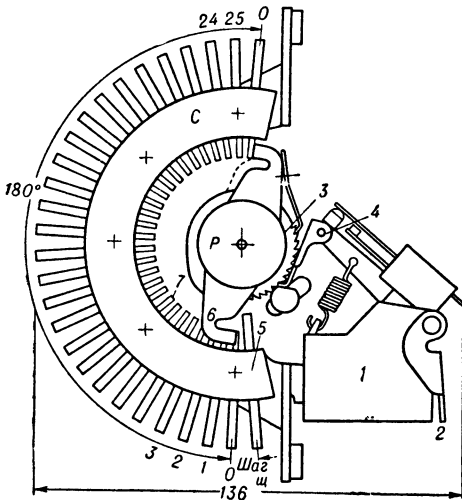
Искатель типа ШИ (эскиз): 1 — катушка электромагнита; 2 — якорь; 3 — храповое колесо; 4 — собачка храпового колеса; 5 — контактная группа; 6 — щетка; 7 — контактная группа.
